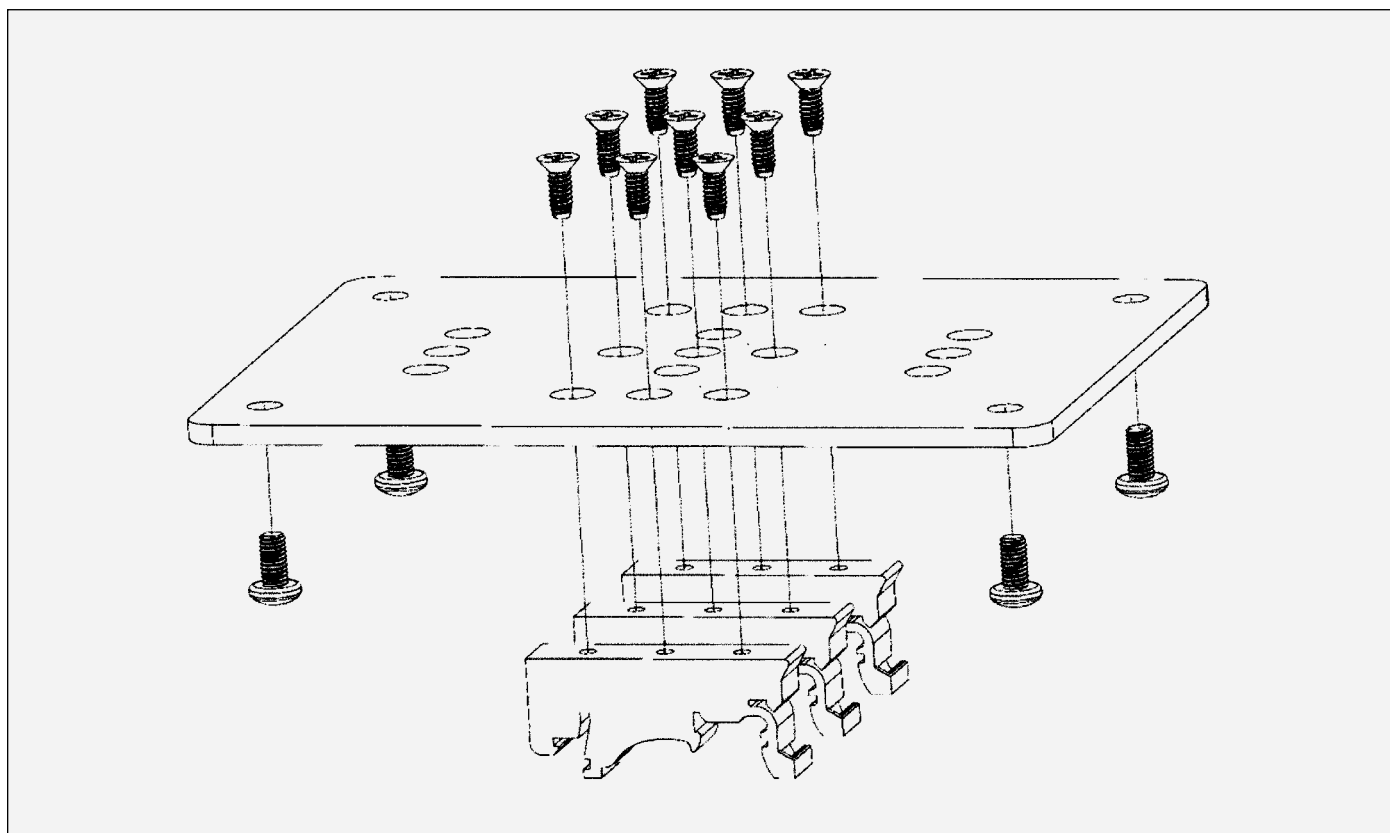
Fissaggio guida DIN del sistema di alimentazione - Configurazione verticale
